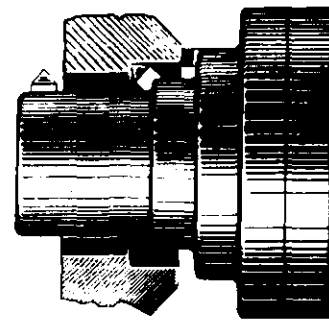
Схема обработки внутренних цилиндрических поверхностей с уступами
